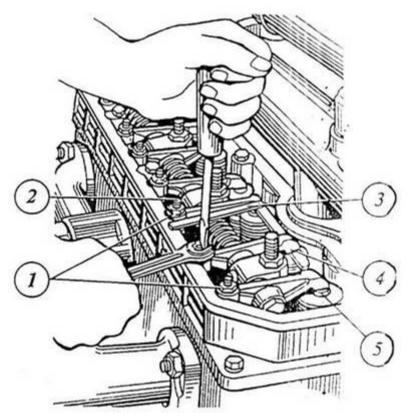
Проверка и регулировка зазоров: 1-контргайка, 2-регулировочный винт, 3-щуп, 4- боек коромысла, 5- стержень клапанов
